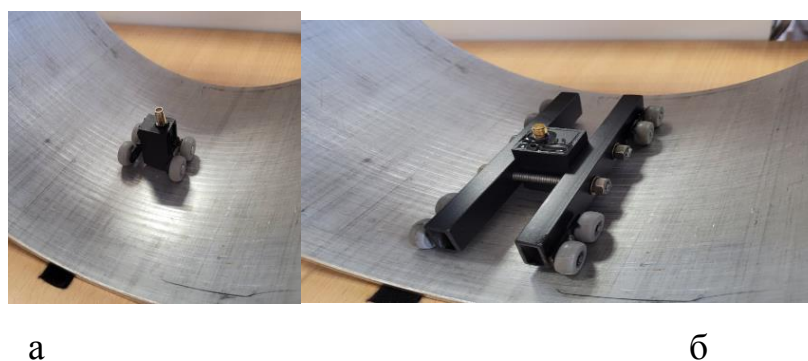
Пьезопреобразователь рэлеевских волн (а), в сборке с направляющей платформой (б)
